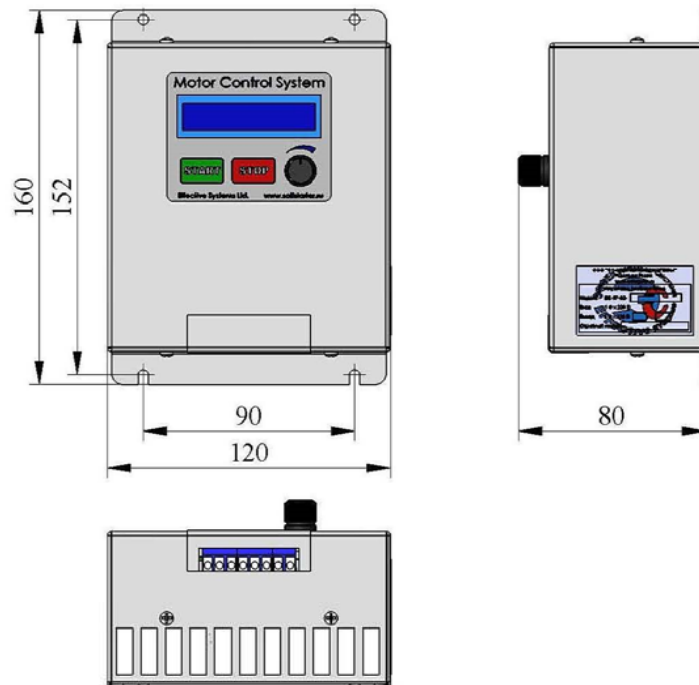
Внешний вид, габаритные и монтажные размеры УПП ES-1P-02
